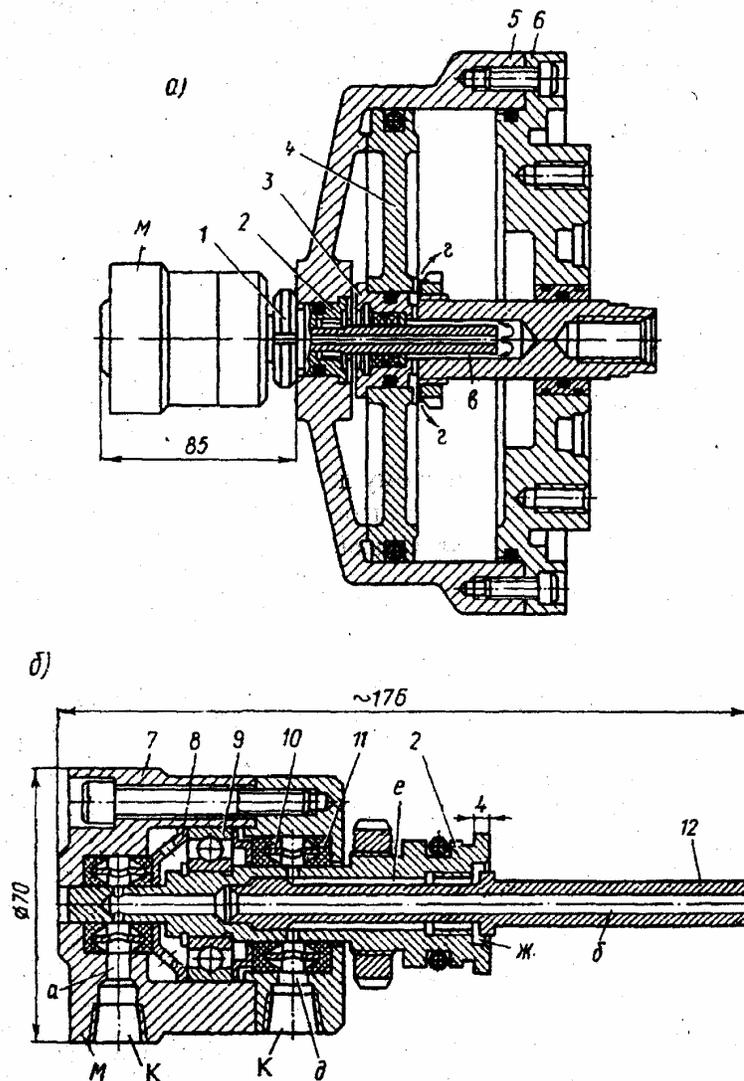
Вращающийся пневмоцилиндр (а) и муфта для подвода воздуха
